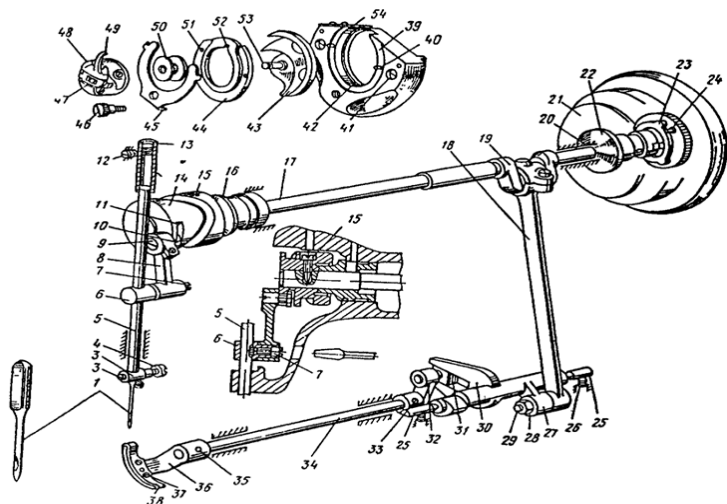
Конструктивная схема механизма иглы, нитепритягивателя и челнока ПМЗ
